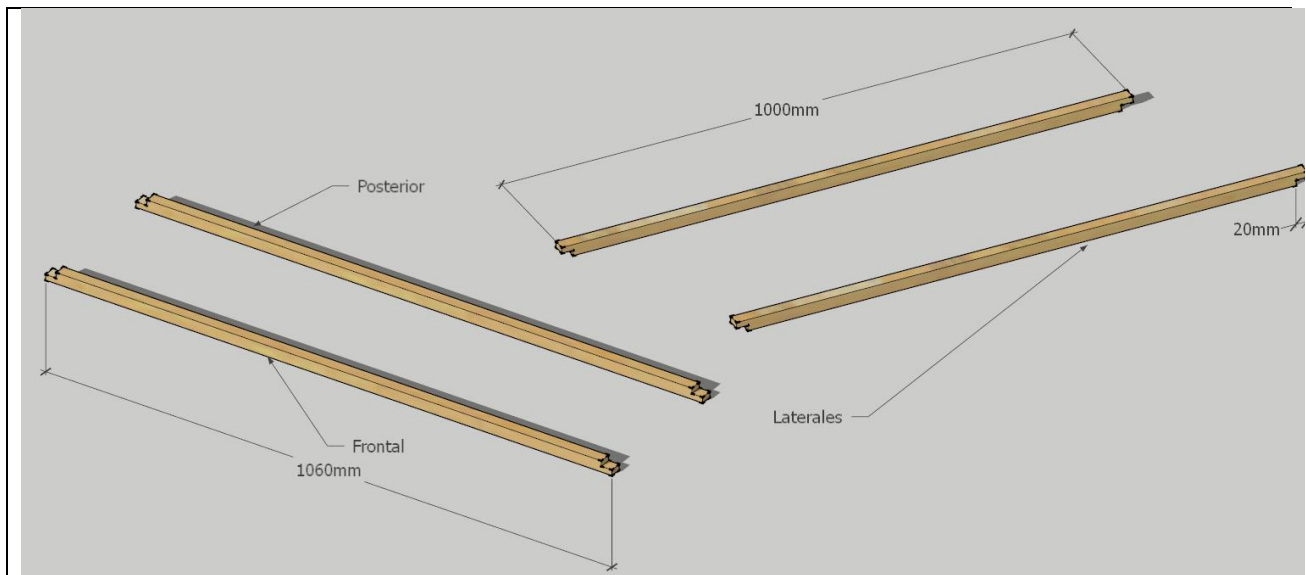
Varillas para la construcción del marco (observar los detalles de los extremos).
